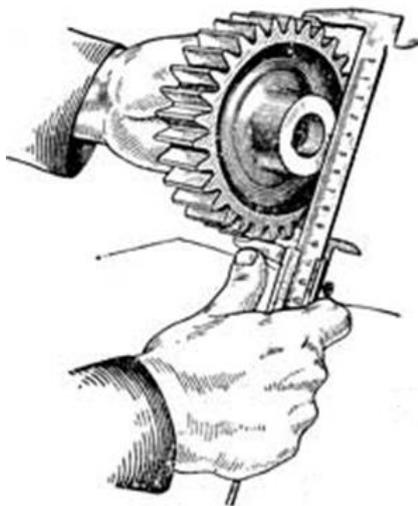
Измерение диаметра зубчатого колеса по головке зуба
